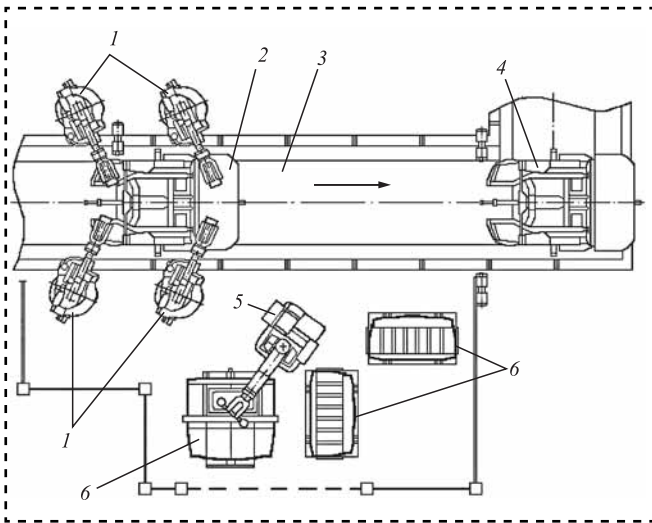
Сборочный модуль приварки крыши к боковинам кузова "ГАЗели" и "Валдая" в составе линии сборки-сварки кабин:
